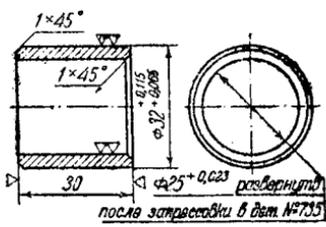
Дет. № 7323. Втулка вала муфты сцепления
